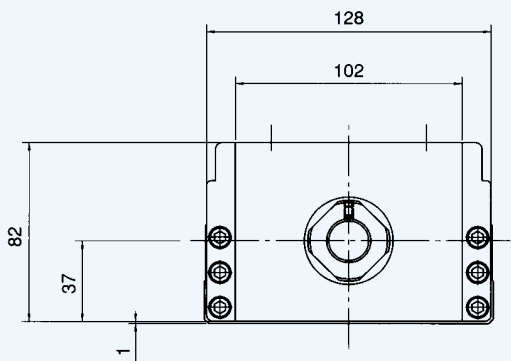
KR65 Housing A ohne Motorflansch (Kennziffer □□10)
